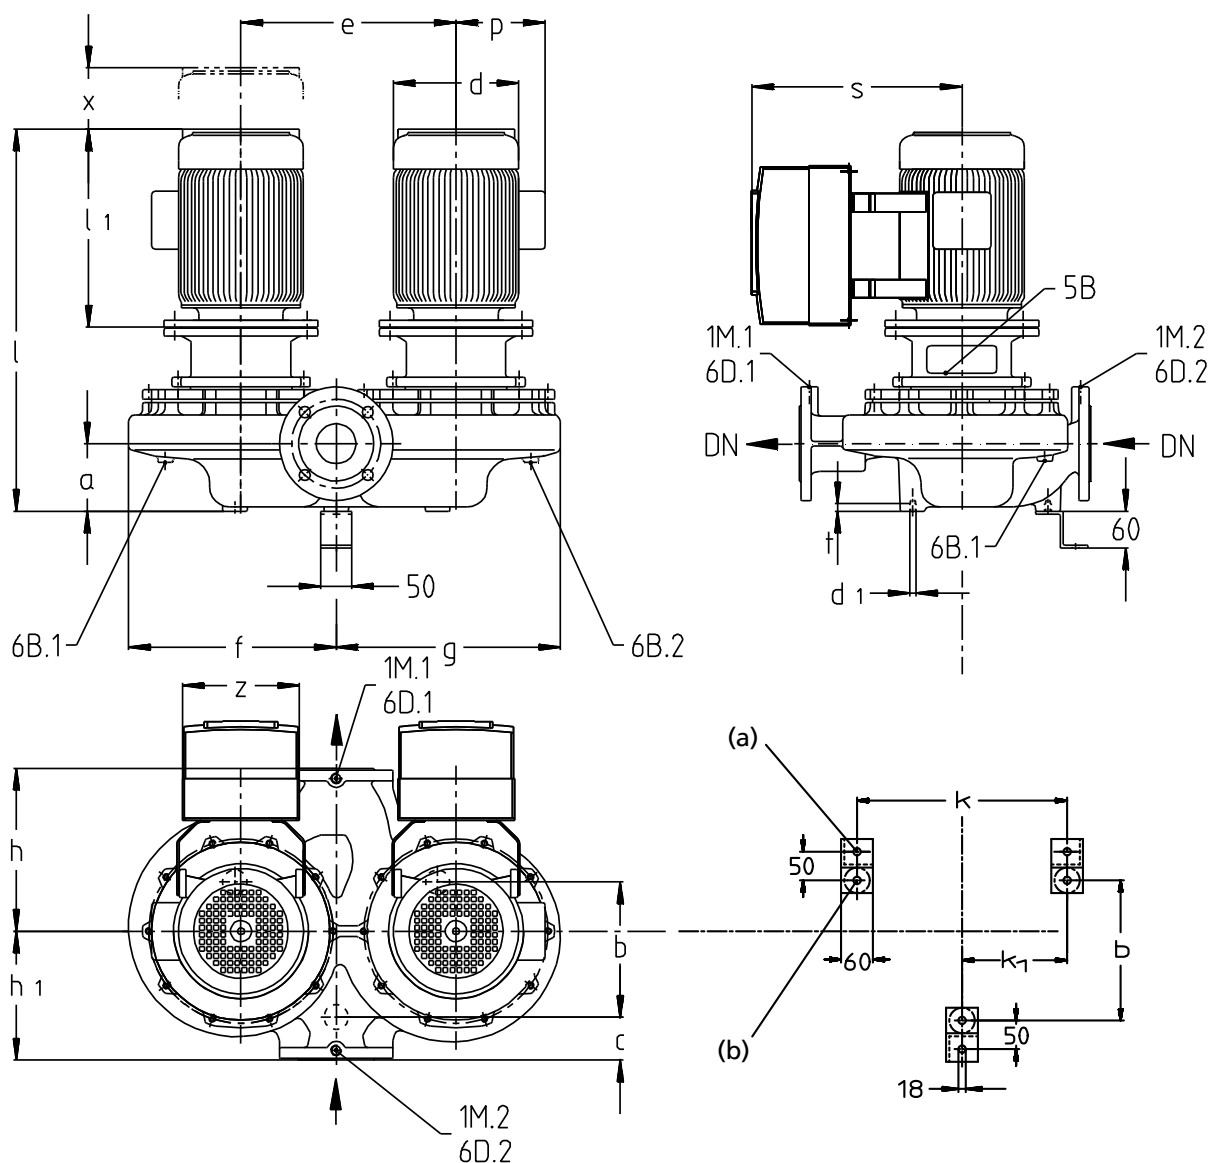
Dimensioni gruppo pompa con PumpDrive 2
